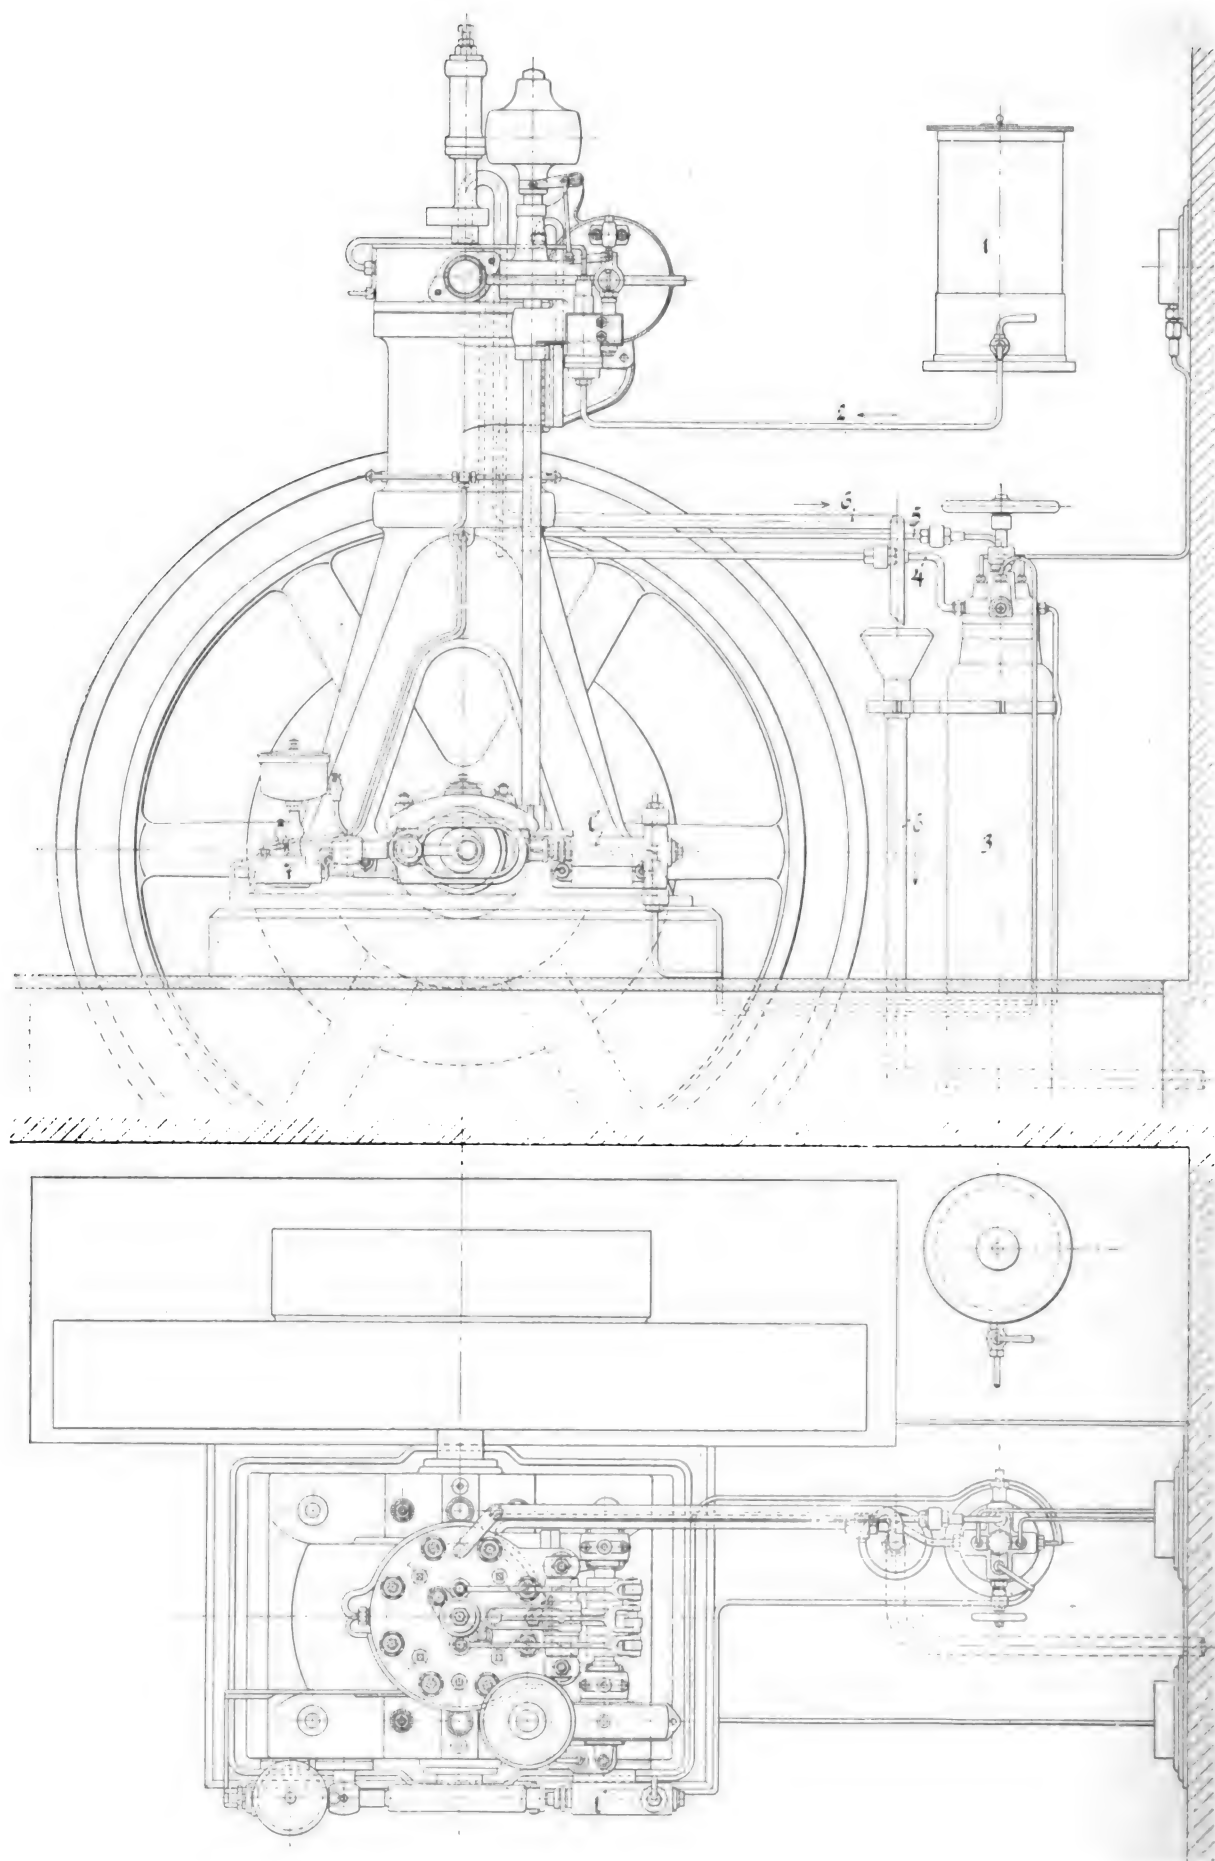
Diesel-Motor der Maschinenfabrik Augsburg.
